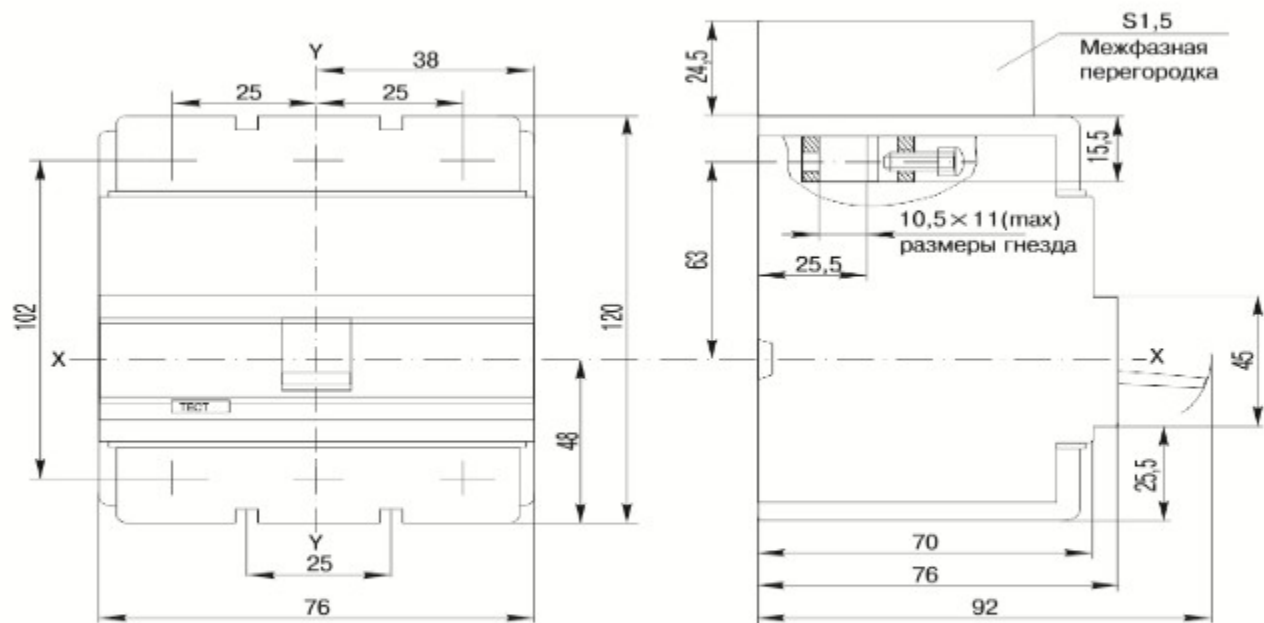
Габаритные и установочные размеры выключателя BA88-32
